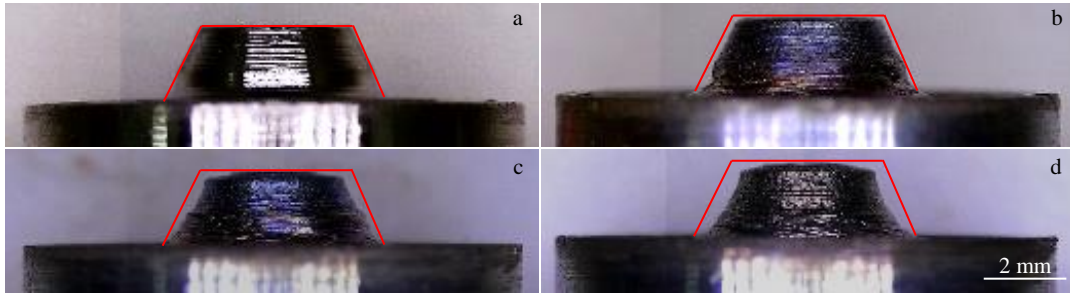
焊接不同距离后搅拌针宏观形貌
